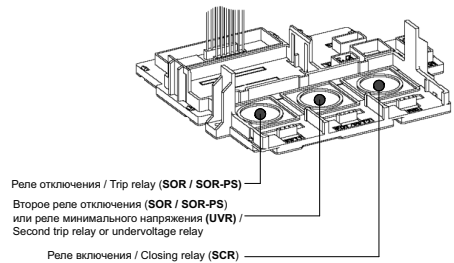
Места установки на плату расширения внутри выключателя / Figure 3 – Locations of mounting on the expansion board inside the circuit-breaker
